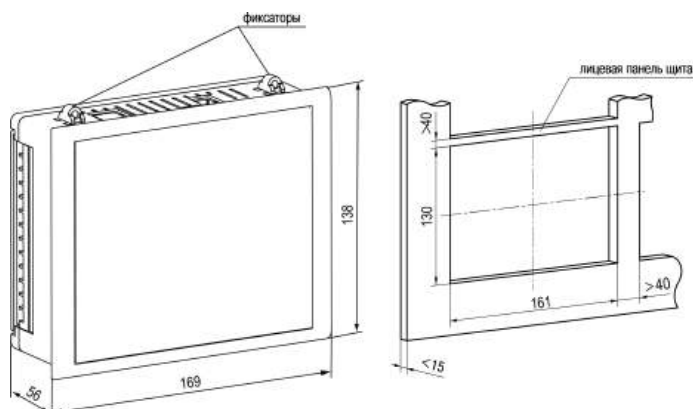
Габаритные размеры корпуса Щ7
